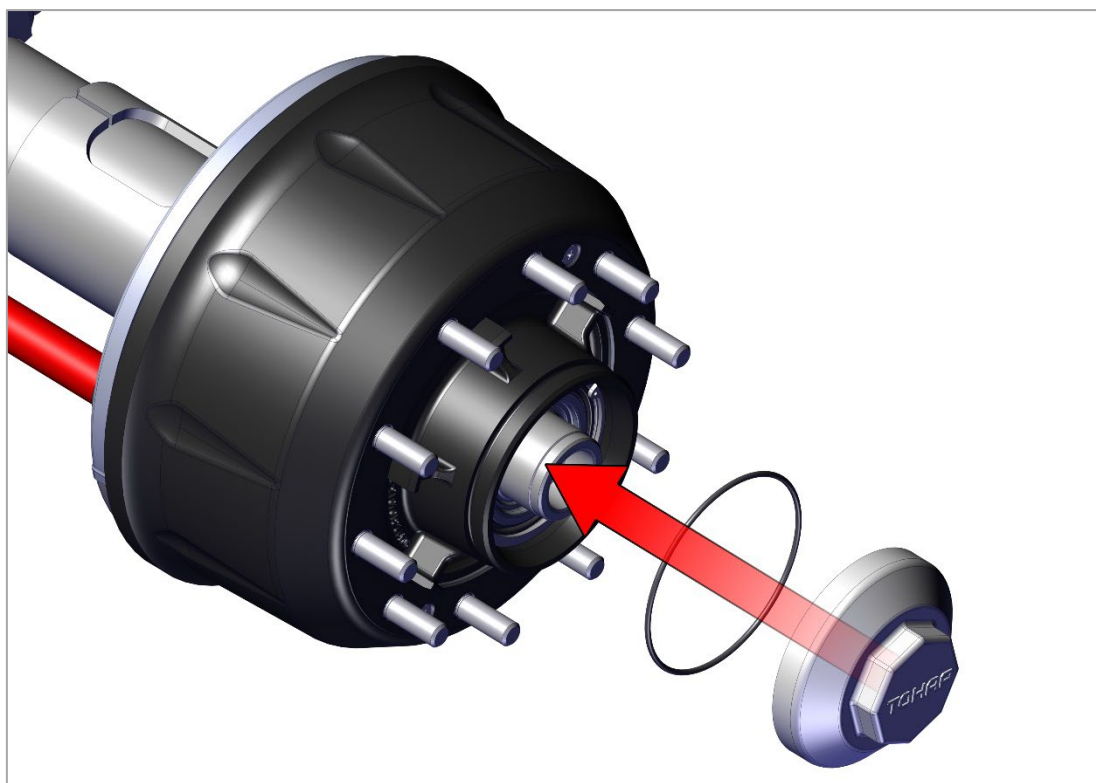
Монтаж крышки ступицы колеса с резиновым уплотнительным кольцом.
